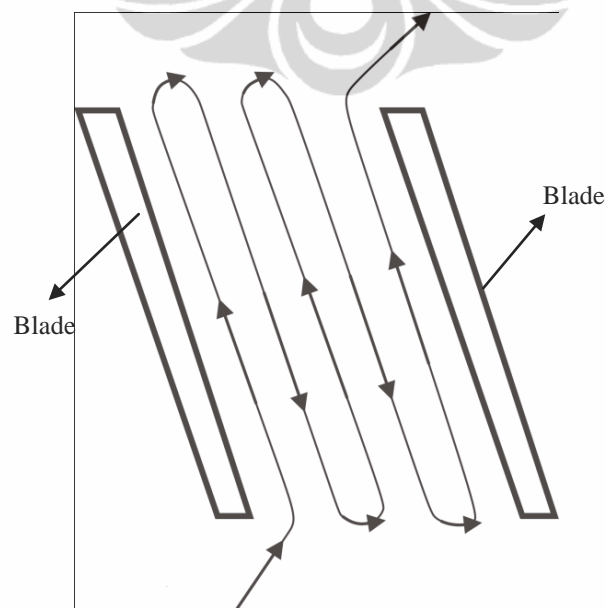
kemungkinan *interference* antara *cutting tool* dengan *workpiece* pada proses *finishing hub* impeller diameter 27 mm
